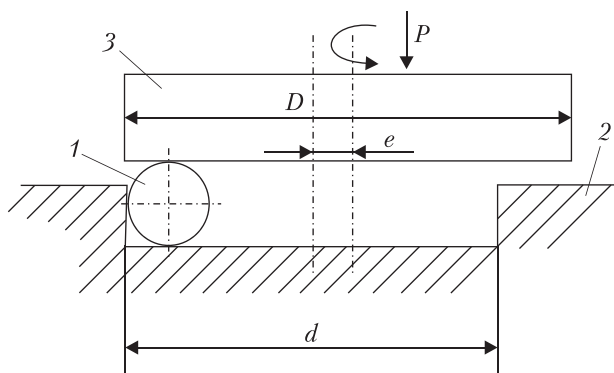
Схема накочування сферичної заготовки плоскими поверхнями
